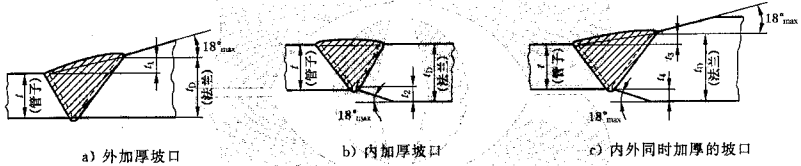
无衬环的对焊法兰的焊接坡口型式及尺寸
